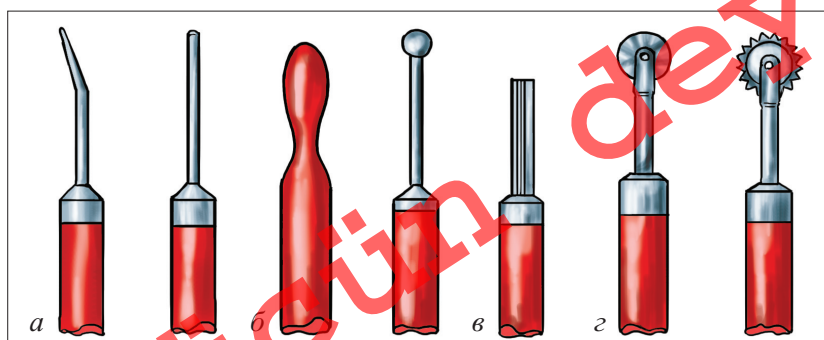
Инструменты для тиснения на фольге: а – линейник; б – выдавка шарообразная; в – пуансон (верхняя часть металло-прокатного штампа); г – накатка
